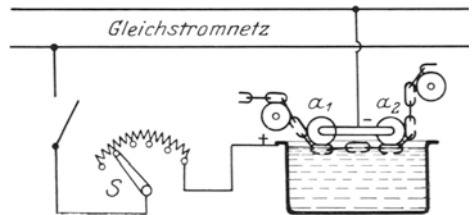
Schweißen von Ketten durch Elektrolyse.
